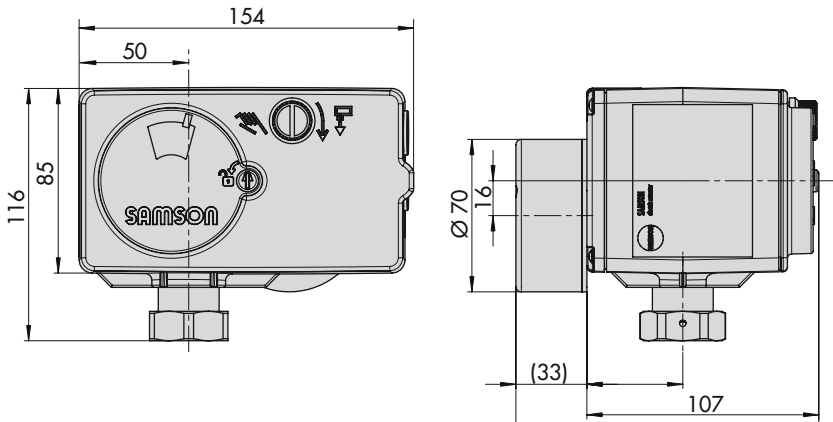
Maße in mm · formschlüssiger Anbau und Schnellläufer
